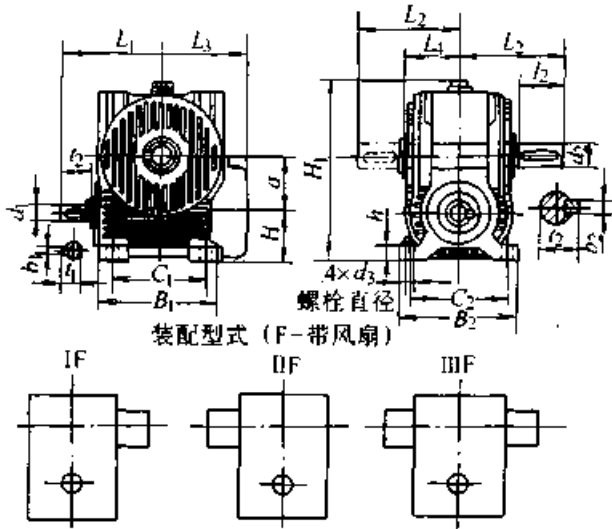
KWU 型减速器的外形尺寸和装配型式
